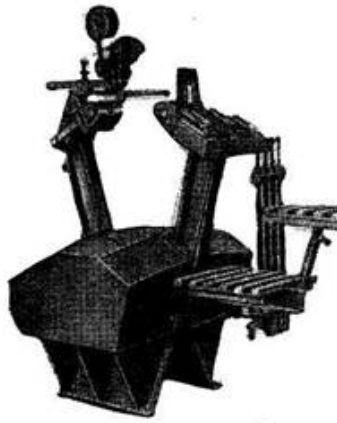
Трубозварювальний обортач, обладнаний головкою ДСГ-7
